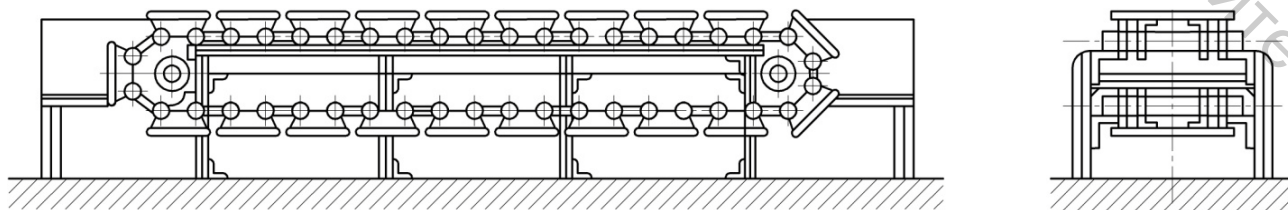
Вертикально-замкнутый тележечный конвейер с опрокидывающимися тележками для сборки автомобильных двигателей
